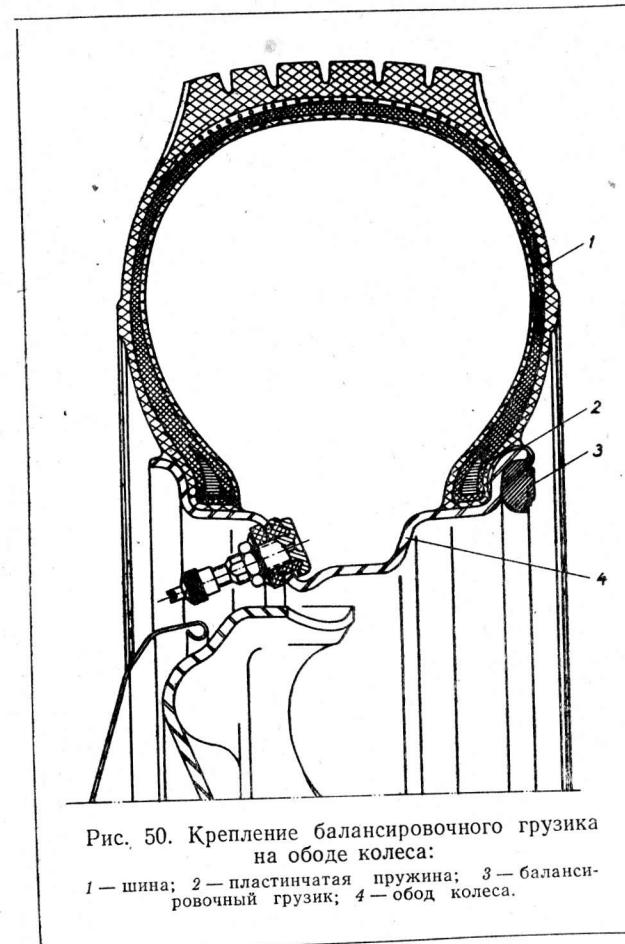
Крепление балансировочного грузика на ободе колеса:
